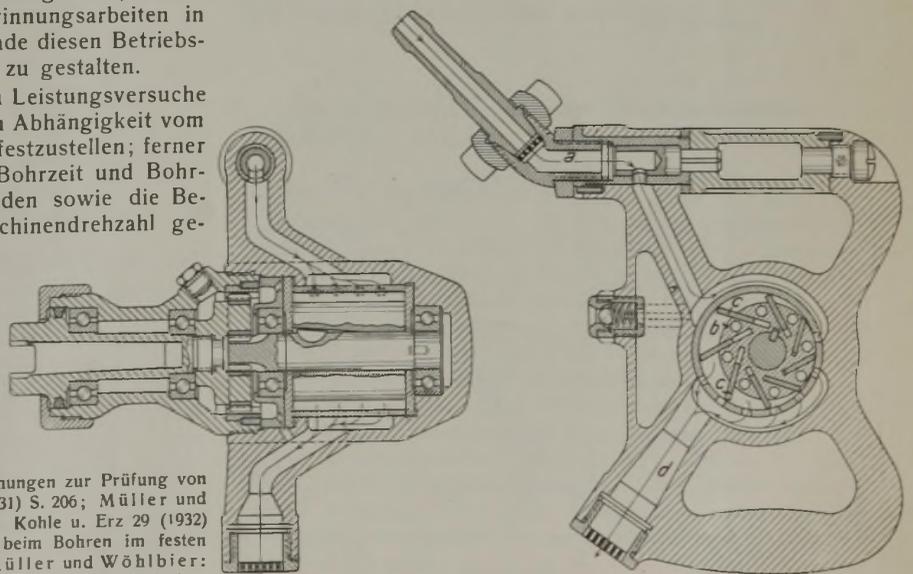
Preßluft-Kohlendrehbohrmaschine.
